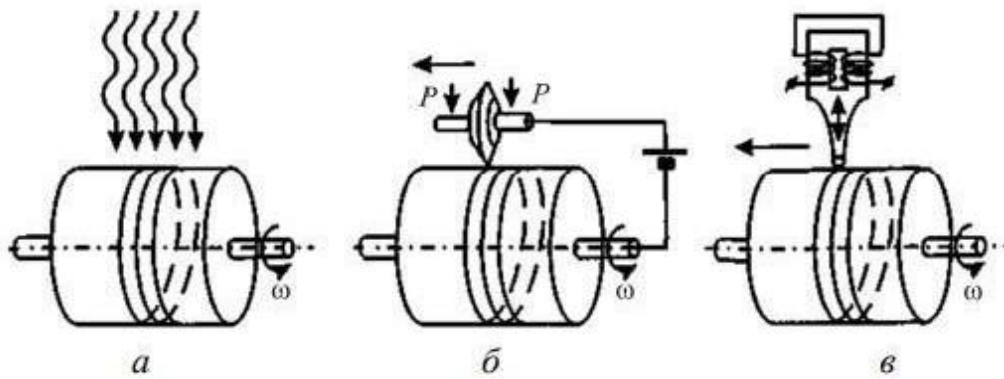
Схеми зміцнення та інтенсивної пластичної деформації приповерхневих шарів: а зміцнення різними видами опромінення та плазмової дії; б обробка з пропусканням струму; в обробка з ультразвуковою дією.  $\omega$  кутова швидкість обертання заготовки
